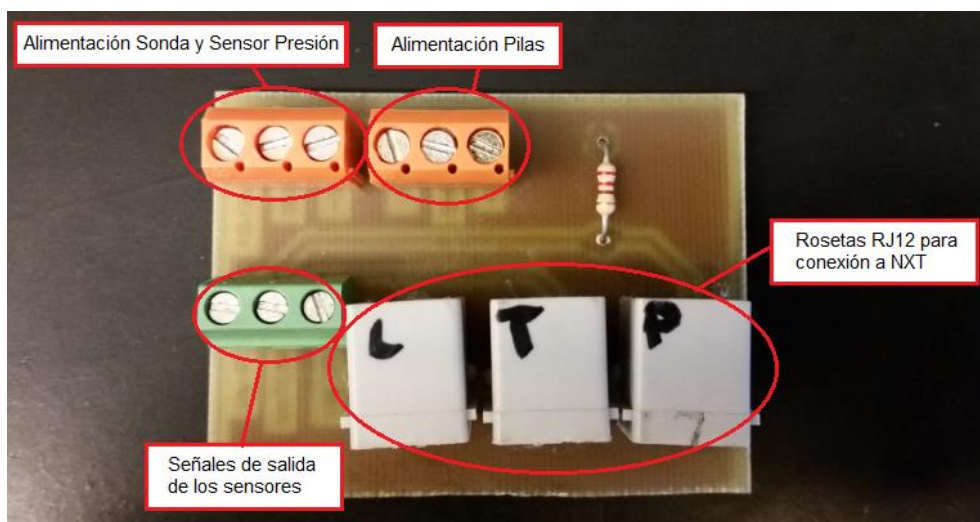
Vista superior y descripción de PCB conexión NXT
